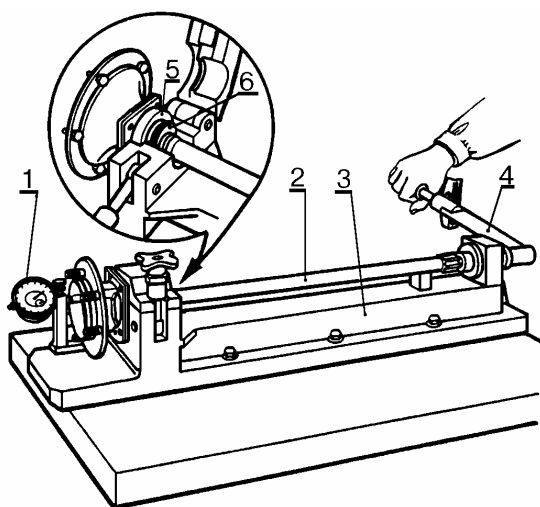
Проверка усилия, с которым выпрессовывается запорное кольцо подшипника полуоси:
